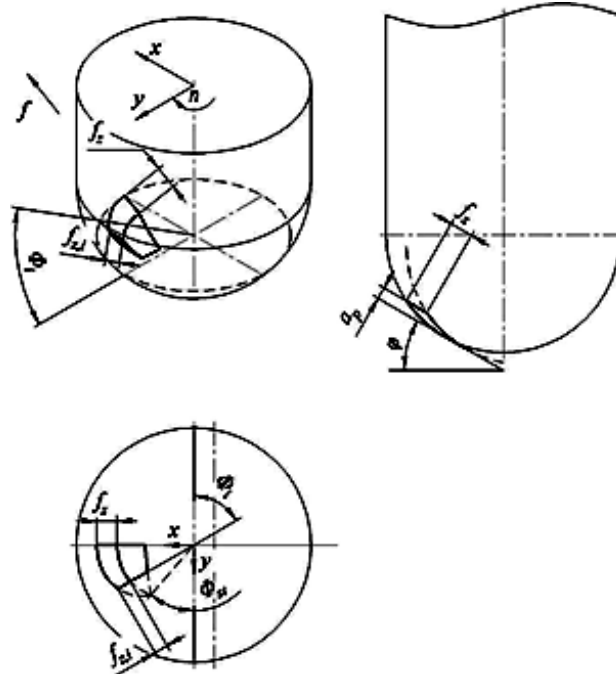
Схема обробки радіусною фрезою похилої поверхні
